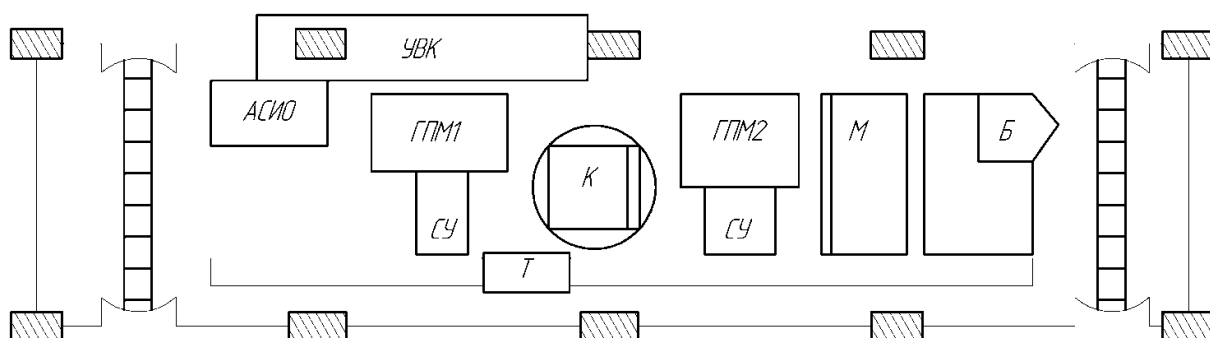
План ГАУ с тяжелыми сверлильно-фрезерно-расточными ОЦ
